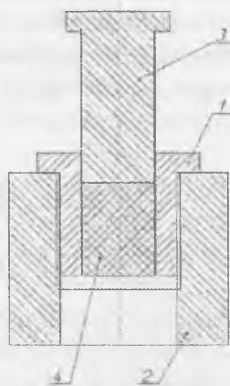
Приспособление в сборе (1 – матрица; 2 – обойма; 3 – шток (пуансон); 4 – опытный композит)
